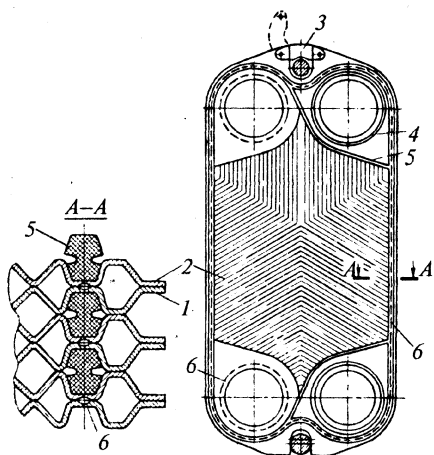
Конструкция попарно сваренных пластин полуразборного аппарата:
